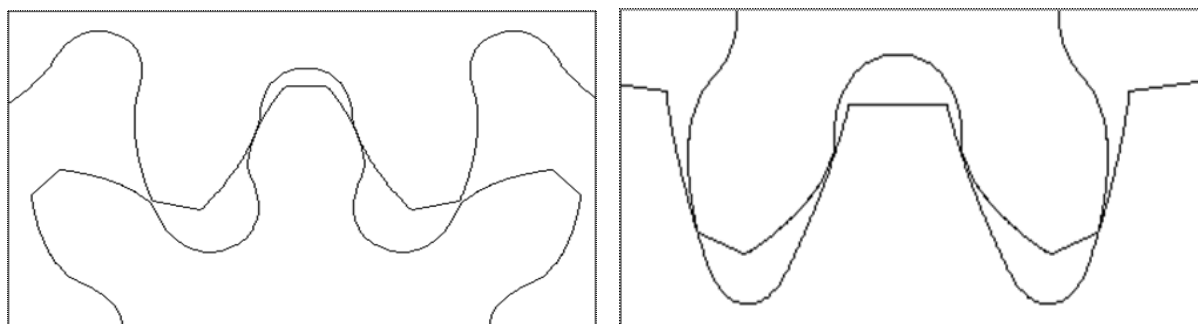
Схема зацеплений минимального сателлита с центральными колесами; коэффициент смещения всех колес  $x = 0$
